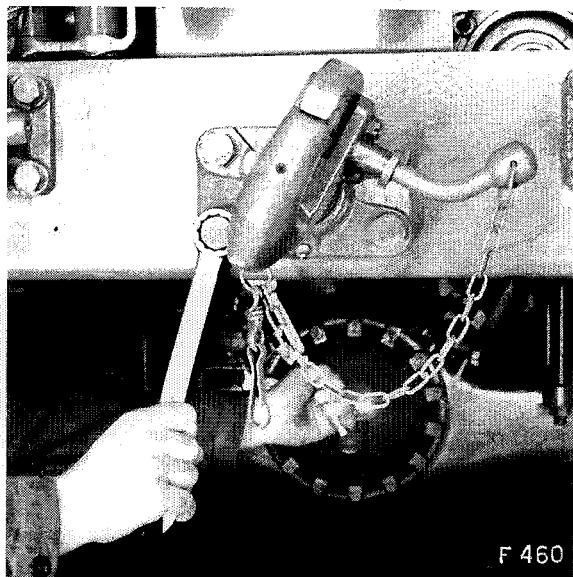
Lösen der Muttern der Befestigungsschrauben für den Anhängenhaken hinten
